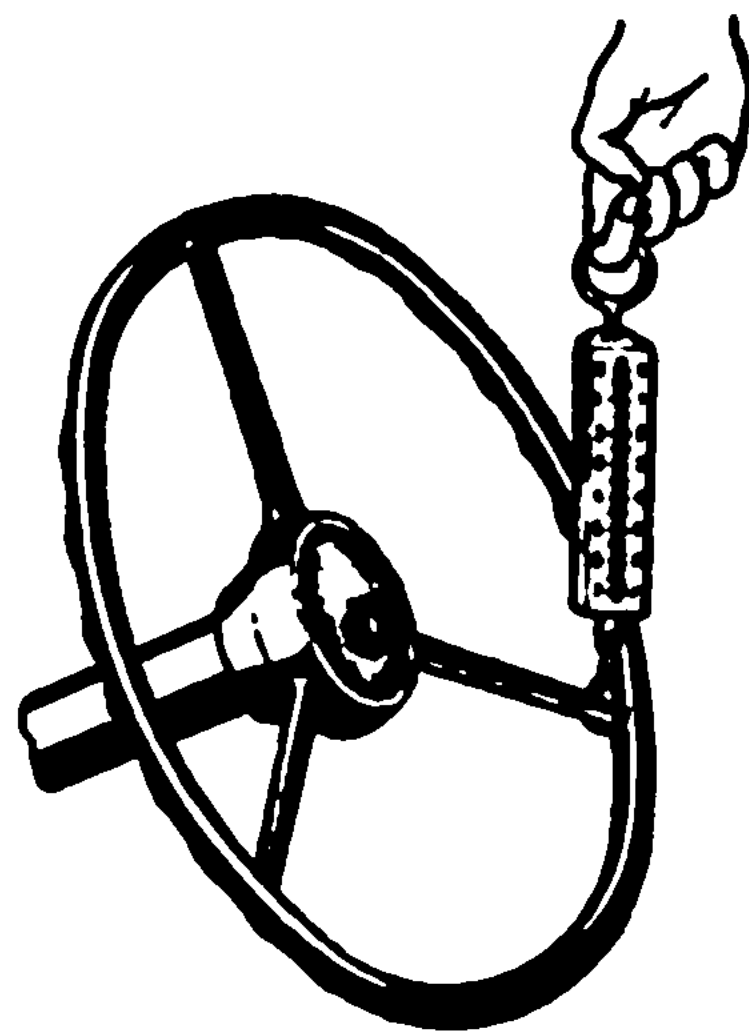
Проверка регулировки рулевого механизма при помощи динамометра
